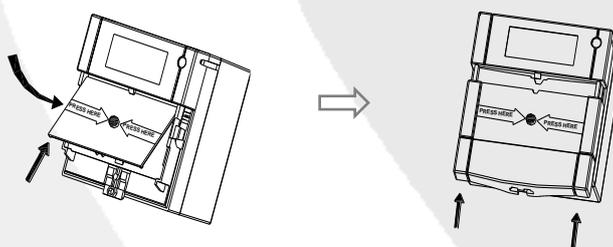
Recoloque o acrílico de operação e a parte frontal
